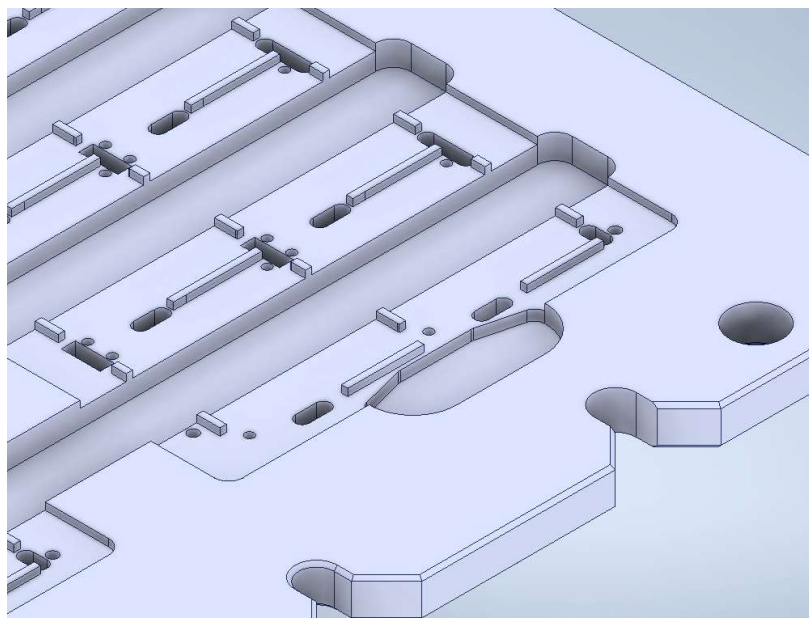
Detail fixačního přípravku [zdroj - vlastní]
